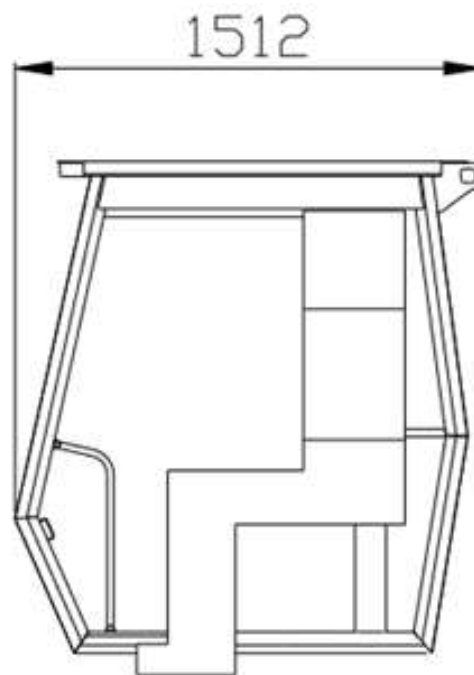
Габаритные размеры кабины (вид сбоку)
